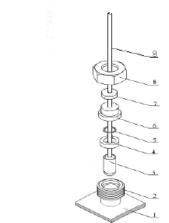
Схема сборки узла УФ датчика. 1 - корпус БО; 2 — патрубок; 3 — датчик излучения; 4 — кольцо уплотнительное; 5 — кольцо из тефлона; 6 — втулка резьбовая; 7 — уплотнитель резиновый; 8 - гайка; 9 — кабель соединительный.
